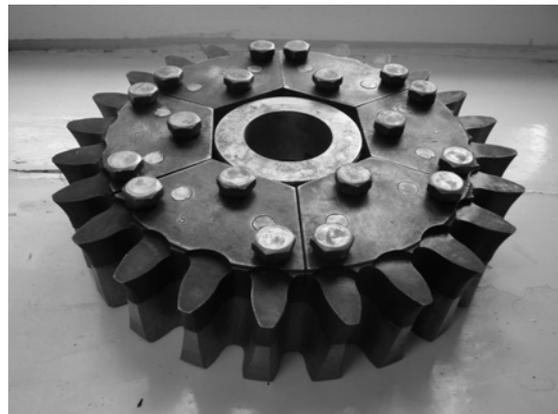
Ротационная резцовая головка для обработки винтовой поверхности на червячной фрезе конволютного типа
